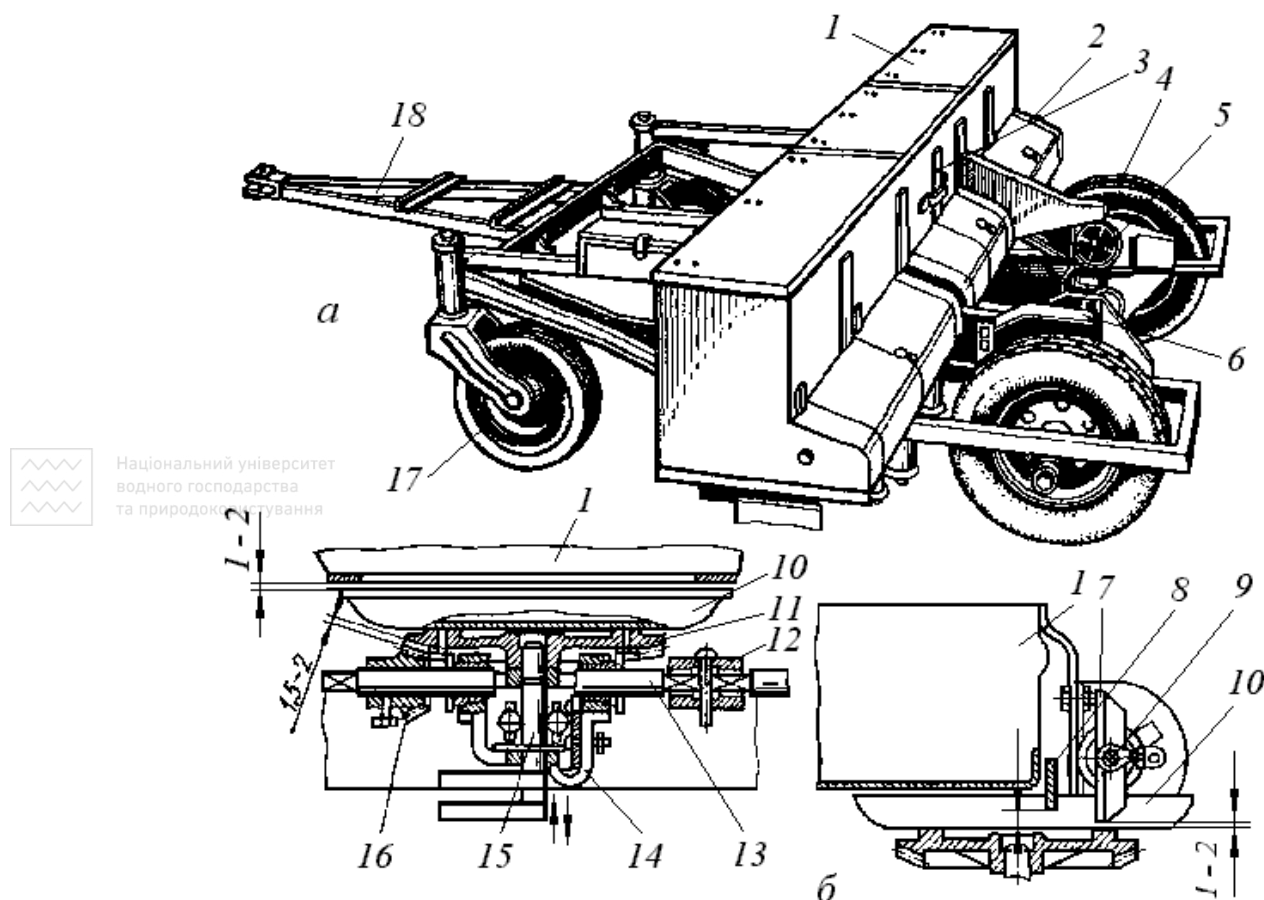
Розкидач-сівалка тукова РТТ-4,2: а - загальний вигляд; б - тарілчастий висівний апарат; 1 - туковий ящик; 2 - захисний щиток; 3 - важіль регулятора висіву; 4 - приводне колесо; 5 - механізм привода на скидачі; 6 - механізм привода висівних тарілок; 7 - скидач; 8 - заслінка регулятора; 9 - вал скидачів; 10 - тарілка; 11 - косозубий вінець тарілки; 12 - муфта; 13 - вал конічних шестерень; 14 - кронштейн; 15 - вісь тарілки; 16 - конічна шестерня; 17 - самовстановне колесо передка; 18 - причіп передка
